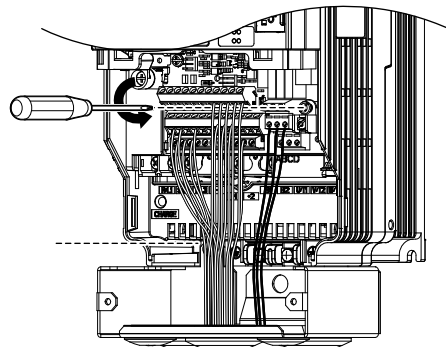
Dévisser la carte de raccordement et retirer le couvercle du dessous
